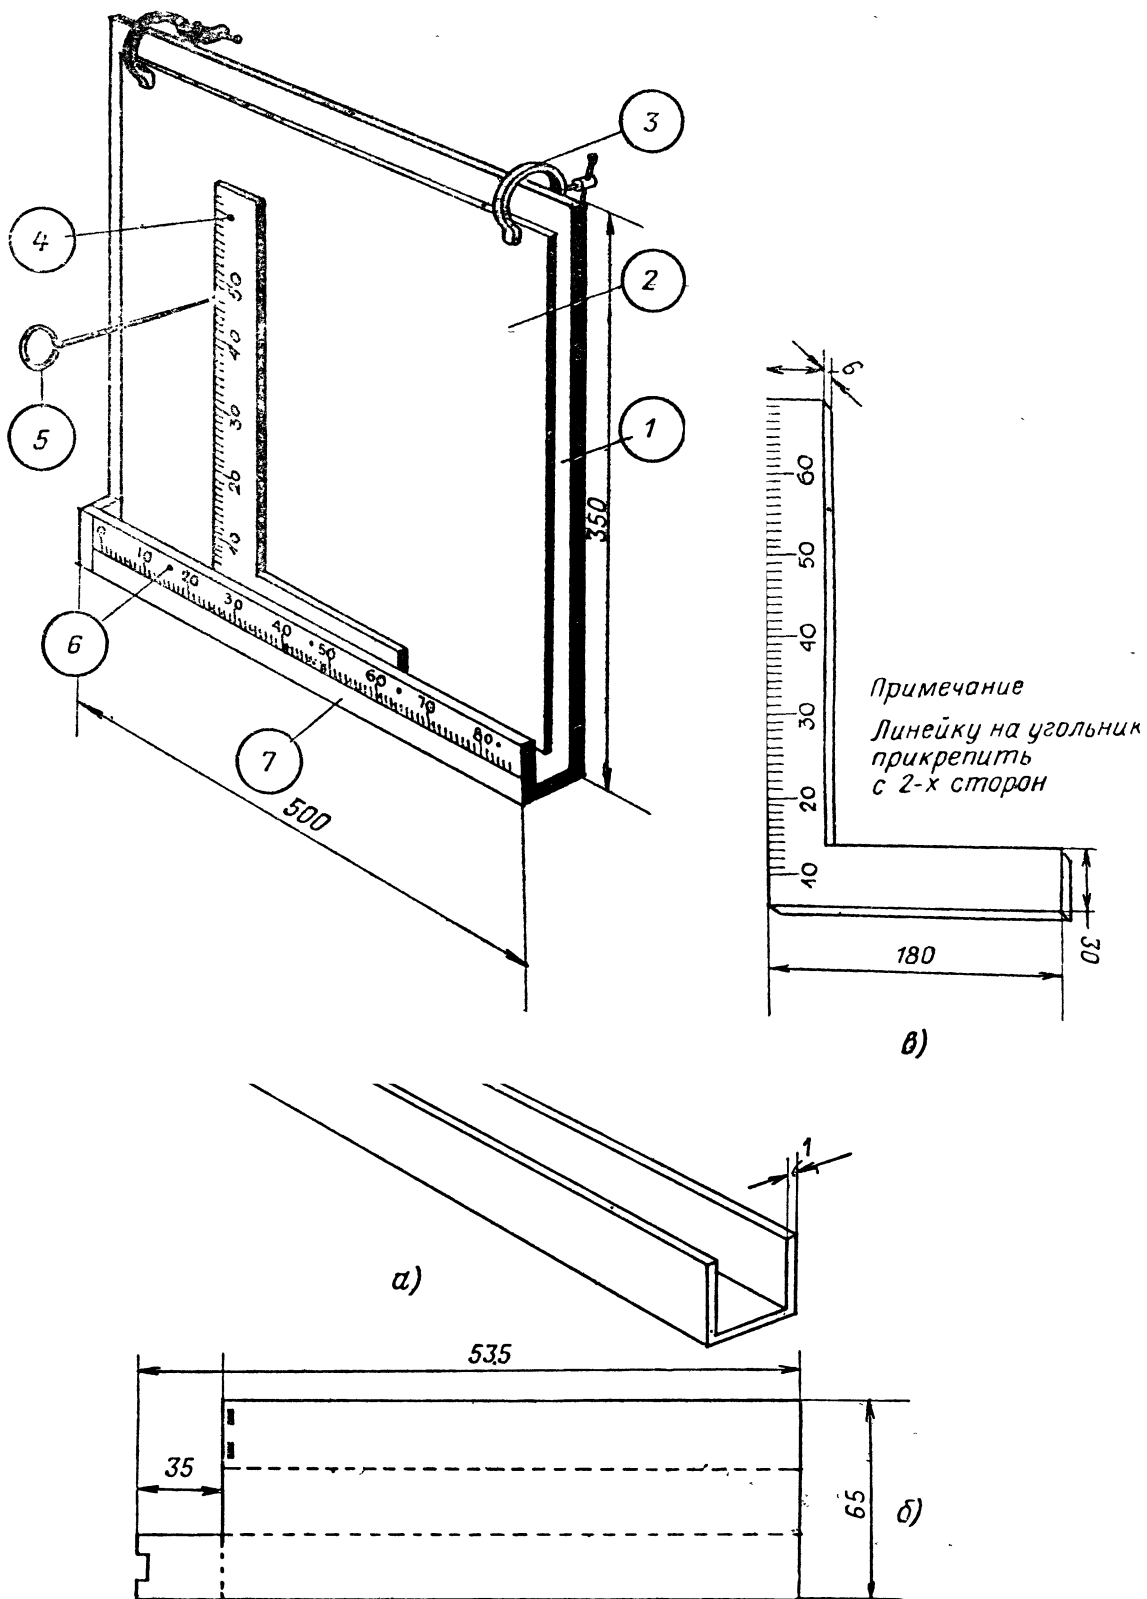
Приспособление для разметки листа: а — упор-каправитель; б — развертка упора; в — разметочный угольник
